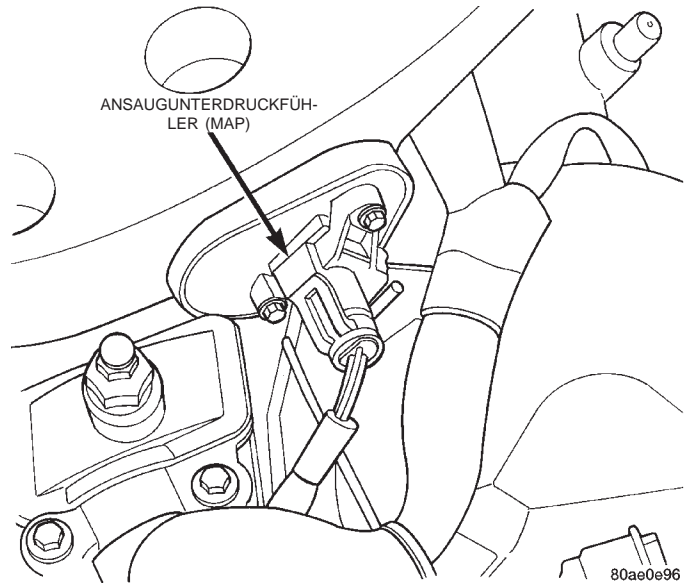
Ansaugunterdruckfühler (MAP) — 2.7L-Motor
